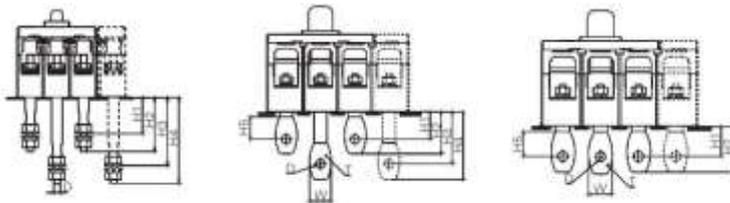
Габаритные размеры задних присоединений ЗП-300Rc
